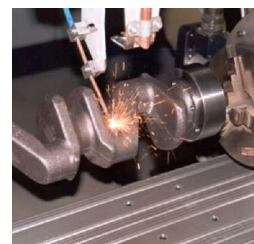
Laserauftragsschweißen an einer Kurbelwelle
